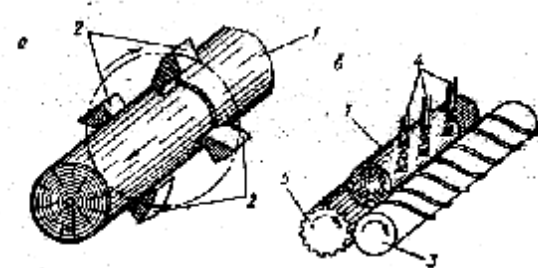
Принципиальные схемы окорки фанерного сырья: а - с помощью ротора с тупыми короснимателями, б - с помощью воды, подаваемой под большим давлением; 1 - окариваемый чурок, 2 - вращающиеся резцы-коросниматели, 3 - винтовой вал для продольного перемещения чурака, 4 - сопла, 5 - рифленый валик для вращения чурака.
